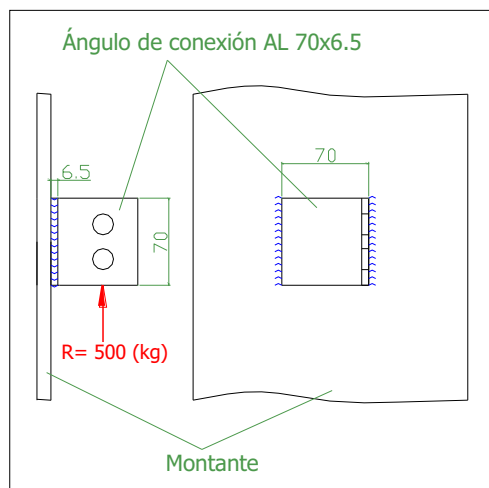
Estado de carga para el análisis de soldadura.
